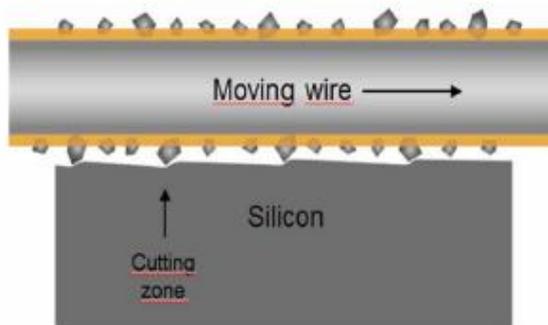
Aufbau des Schnitt-Drahtes © Meyer Burger AG
